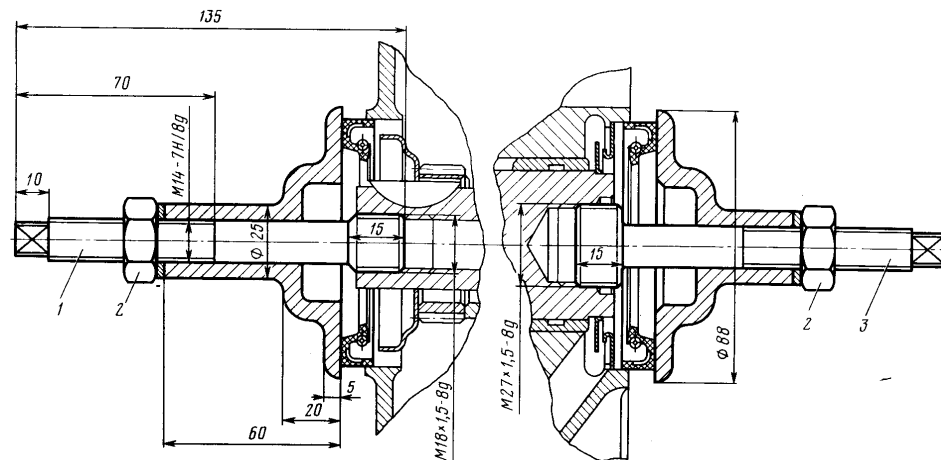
Оправка для установки манжет коленчатого вала: 1 и 3— винты; 2 — гайка.
